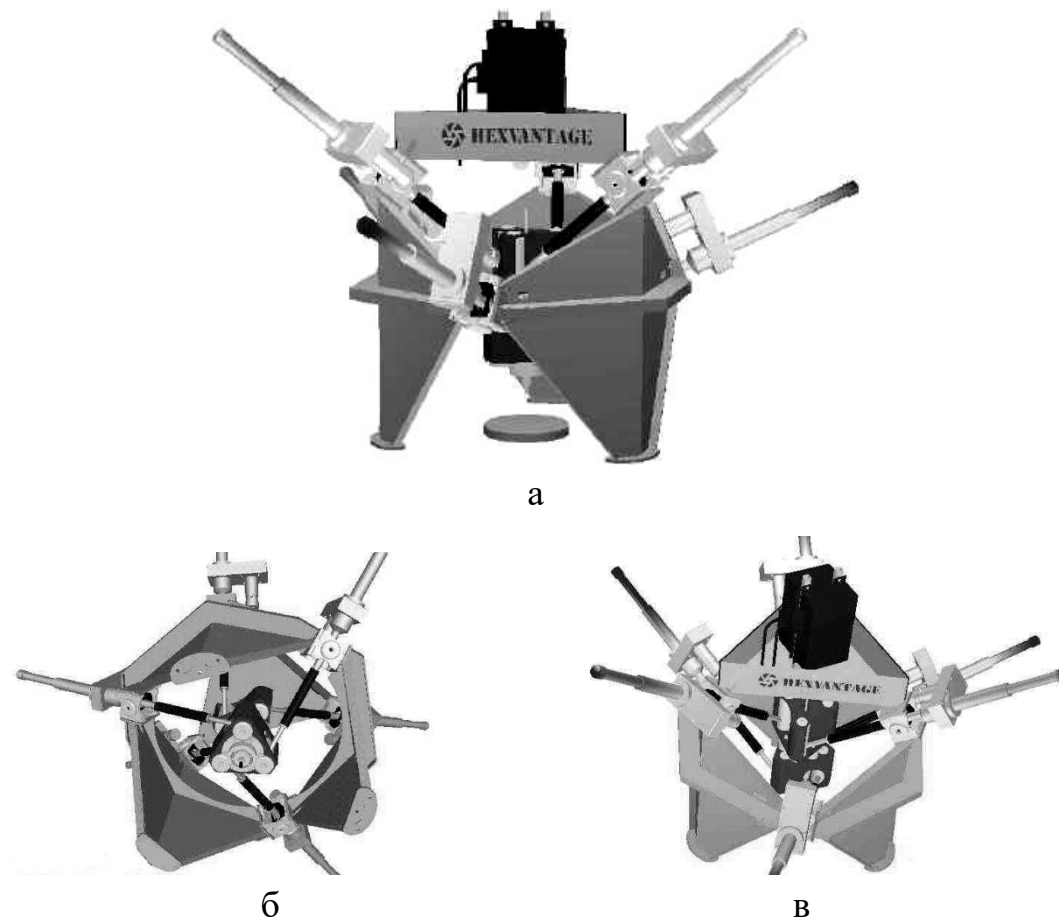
П'ятикоординатний верстат-гексапод мод. HEXVANTAGE фірми PATHFINDERS INCORPORATED (США) (а) і його робоча зона: б – вид знизу; в – вид зверху
